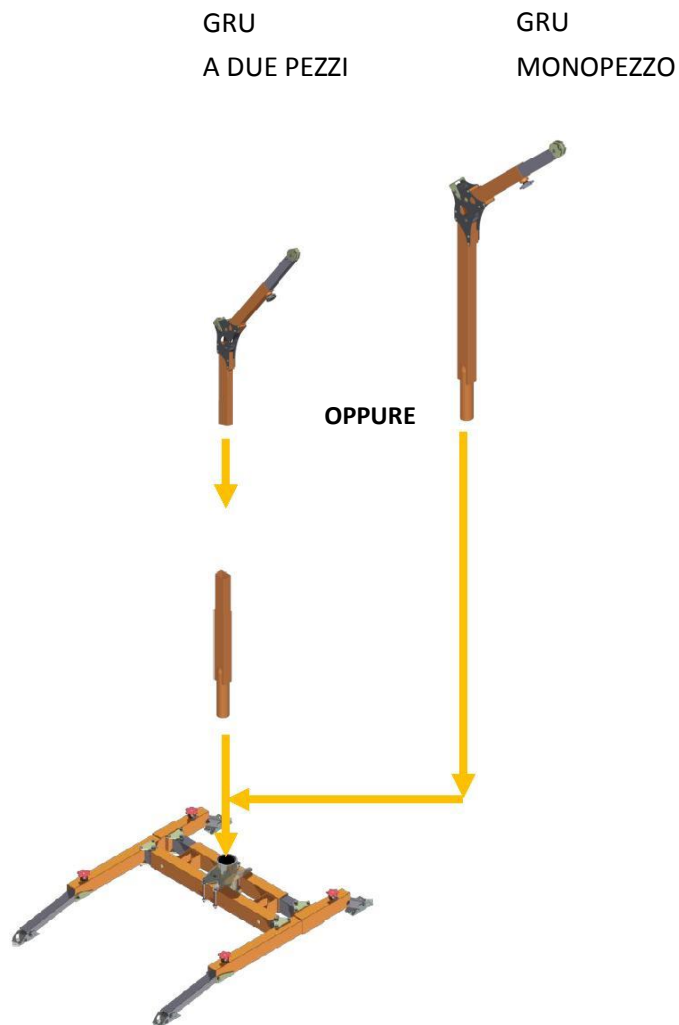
, Installazione del braccio nella base di fissaggio della serie DAVIT 1000
